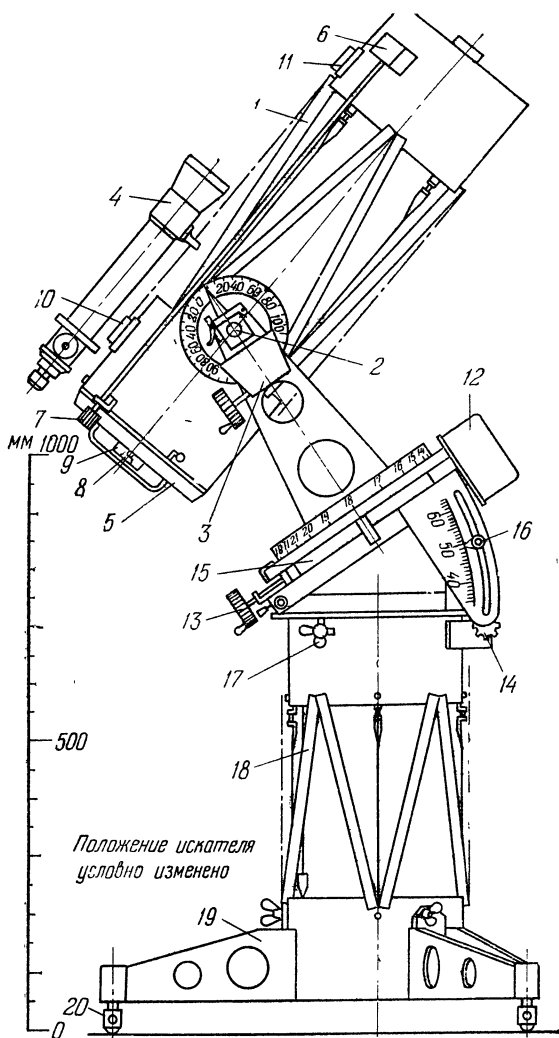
Конструктивный чертеж телескопа УПТР-10: 1—труба, 2—полуоси и подшипники вращения вокруг оси склонений, 3—механизм и ручка управления оси склонений, 4—искатель, 5—чашка с оправой главного зеркала, 6—механизм для перемещений вторичного зеркала, 7—ручка фокусировки, 8—кнопки открытия крышки главного зеркала, 9—окулярная часть для системы Кассегрена, 10—окулярная часть для системы Ньютон, 11—окулярная часть системы Нессмита, 12—электропривод часовой оси, 13—ручка управления вращением вокруг часовой оси, 14—устройство для коррекции положения часовой оси по азимуту (для установки в меридиане), 15—подшипник качения часовой оси, 16—устройство для установки телескопа под нужным углом широты места наблюдения, 17—фиксирующие зажимы узла осей на колонне, 18—колонна установки, 19—съемные опоры, 20—регулирующие винты установки по отвесу или ватерпасу.
